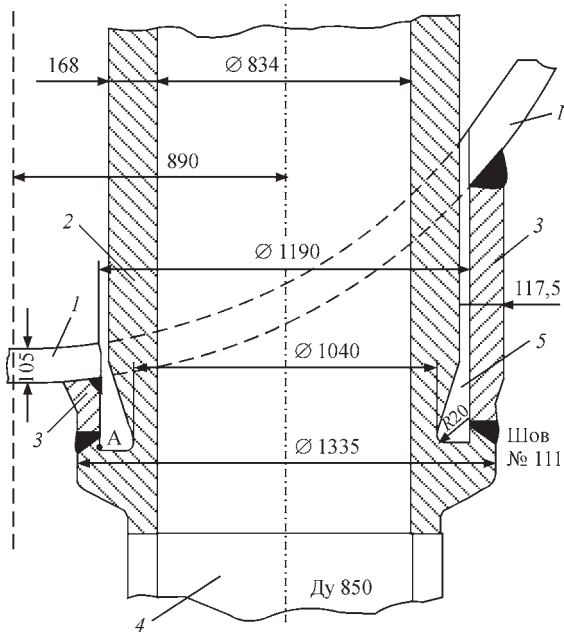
Схема розташування зварного з'єднання № 111: 1 – корпус парогенератора; 2 – колектор; 3 – патрубок Ду1200; 4 – трубопровід Ду850; 5 – карман; А – дефект несущієності
